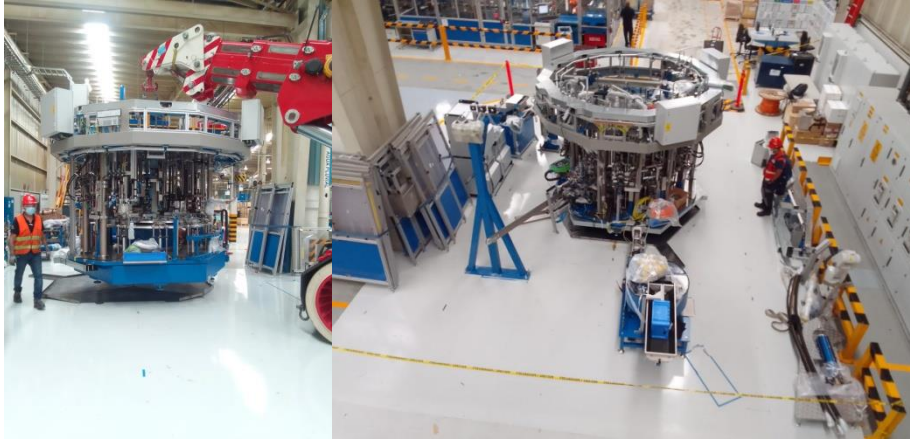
Parte principal de la máquina, manipulada por medio de la grúa hidráulica.
